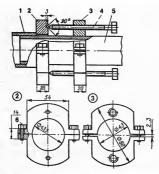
Разъединение труб: 1— наружная труба; 2— подвижный хомут; 3— неподвижный хомут; 4— болт М10—80; 5— внутренняя труба; 6— внит М8—16 (размеры приведены для «Жагулев»).
